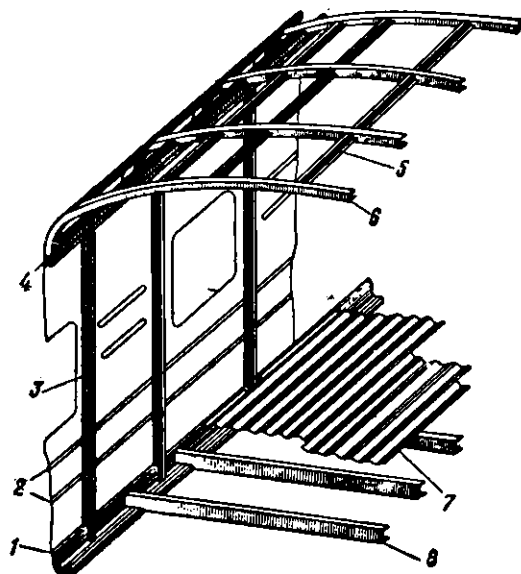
Конструкция кузова цельнометаллического вагона без хребтовой балки; 1 — нижняя обвязка; 2 — продольные гофры; 3 — стойка; 4 — верхняя обвязка; 5 — стрингеры крыши; 6 — дуга крыши; 7 — гофрированная обшивка; 8 — нижние поперечные балки
